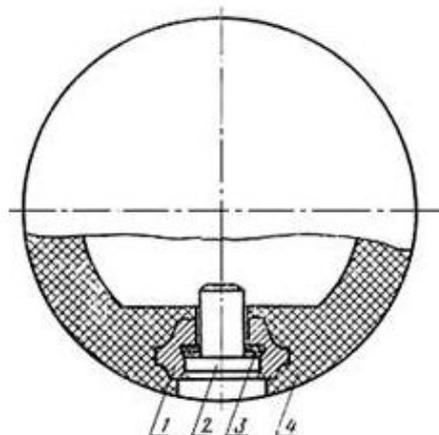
Конструкция полиуретанового шара: 1 - обойма; 2 - клапан; 3 - прокладка; 4 – оболочка.
